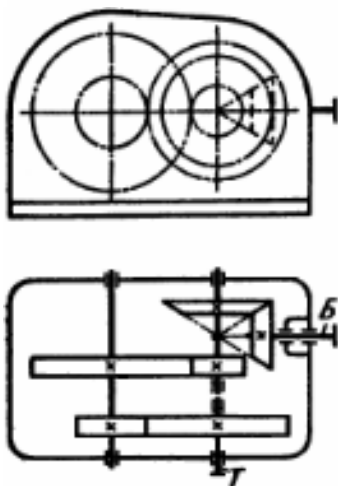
Коническо-цилиндрический трехступенчатый горизонтальный редуктор с соосными цилиндрическими ступенями
